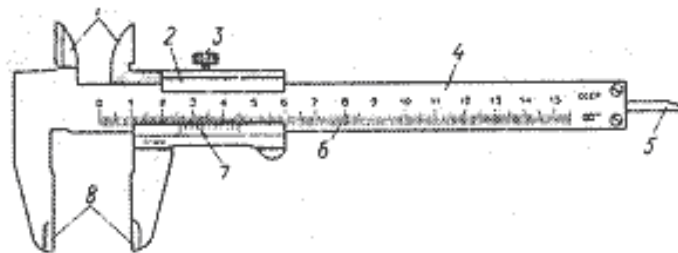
Штангенциркуль ШЦ-1 з діапазоном вимірювання 0–125 мм і величиною відліку 0,1 мм. 1 – губки для внутрішніх вимірювань, 2 – рамка, 3 – затиск рамки, 4 – штанга, 5 – лінійка глибокометра, 6 – шкала штанги, 7 – ноніус, 8 – губки для зовнішніх вимірювань
